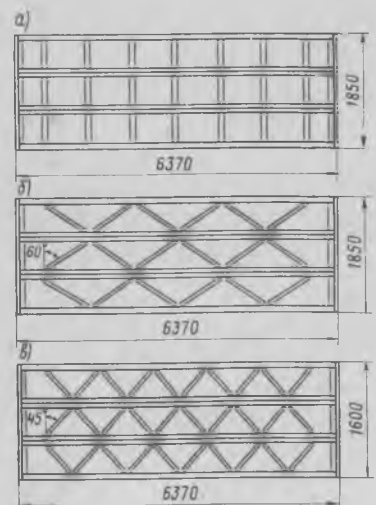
Балочные решетки поддонов для изготовления многосустотных панелей перекрытия с преднапряженной арматурой
